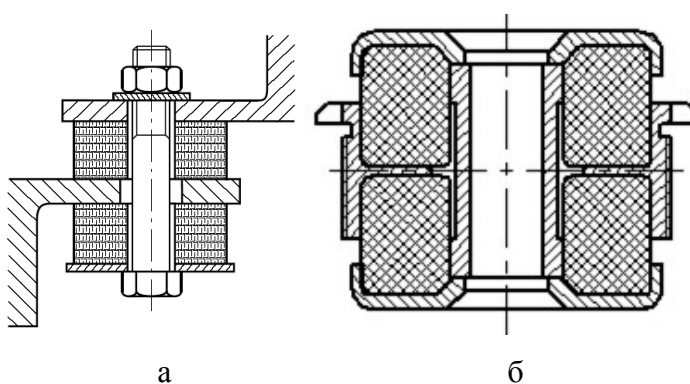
Виброизоляторы втулочного типа: а – бескорпусной, б - корпусной
